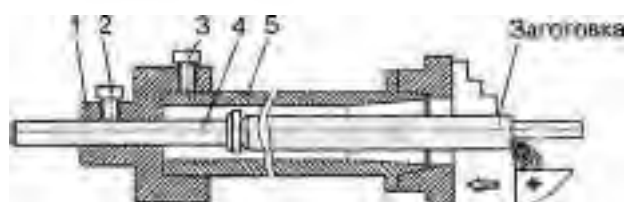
ВИКОРИСТАННЯ УПОРНОЇ ШТАНГИ
